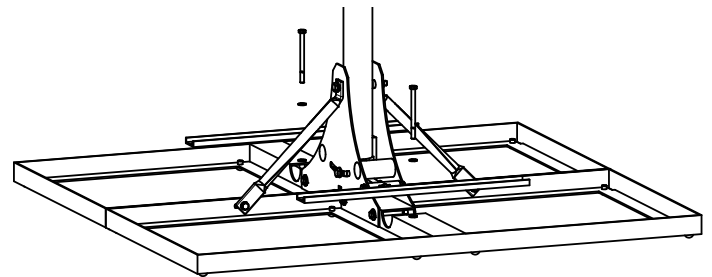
Schienen zur Sicherung der Betonplatten befestigen
